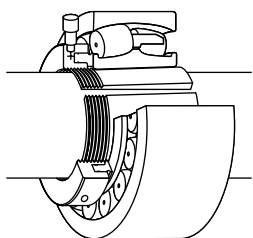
Écrou hydraulique utilisé pour monter le roulement sur un manchon de serrage.
